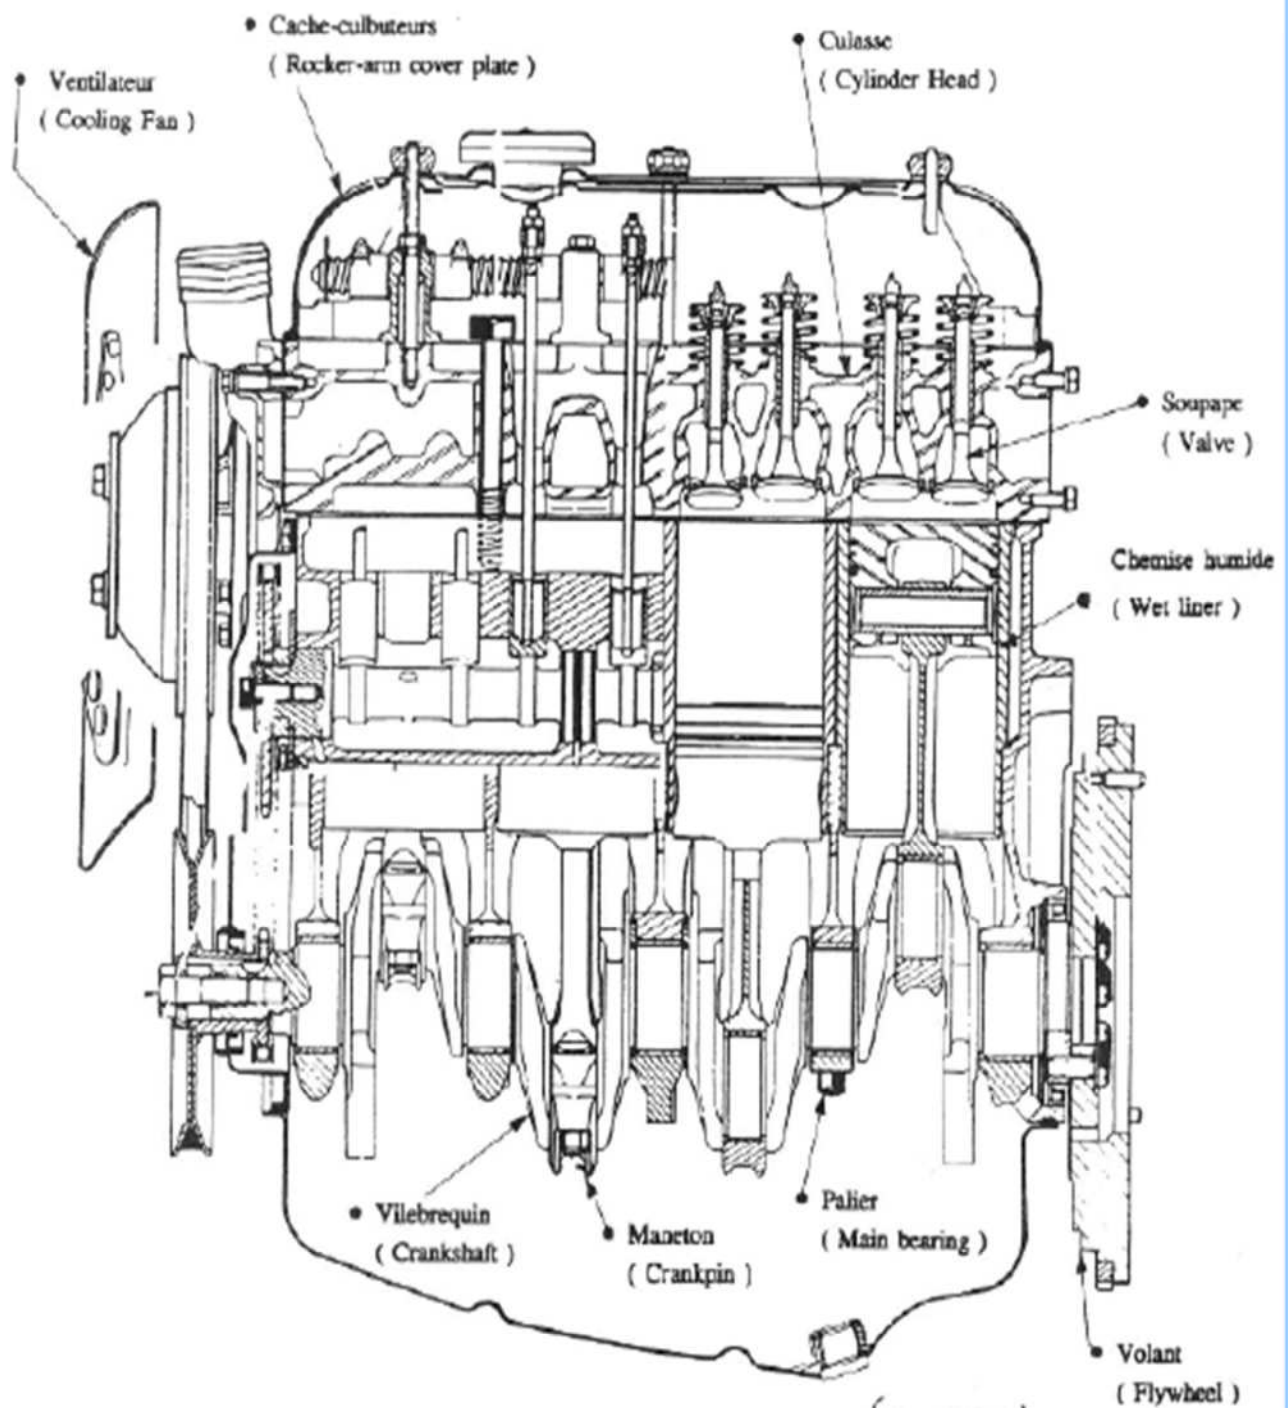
Schéma d'ensemble d'un moteur thermique [6].
